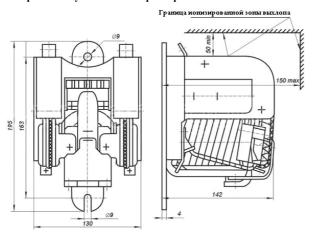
Габаритные, установочные размеры КПД-121 У2
